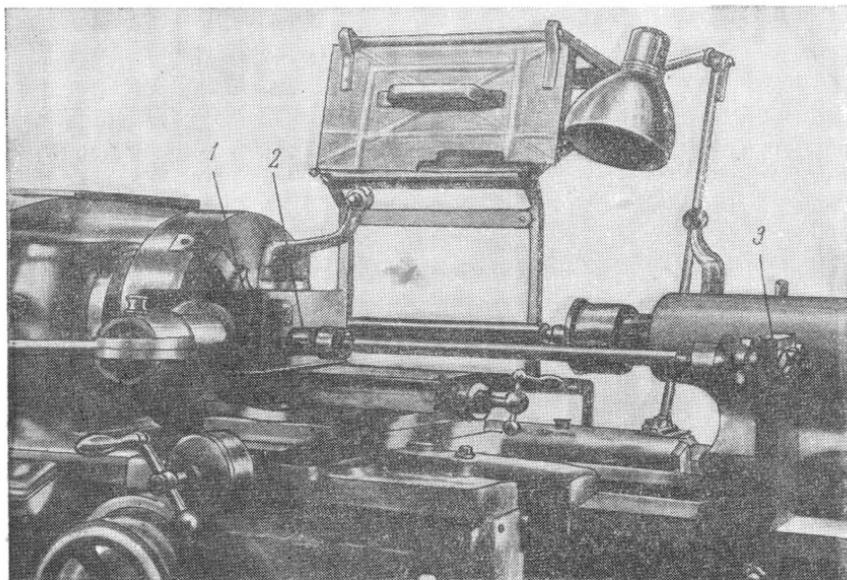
Гидросуппорт крупного токарного станка „Волленберг“ (на станке обрабатывается деталь весом около двух тонн).
